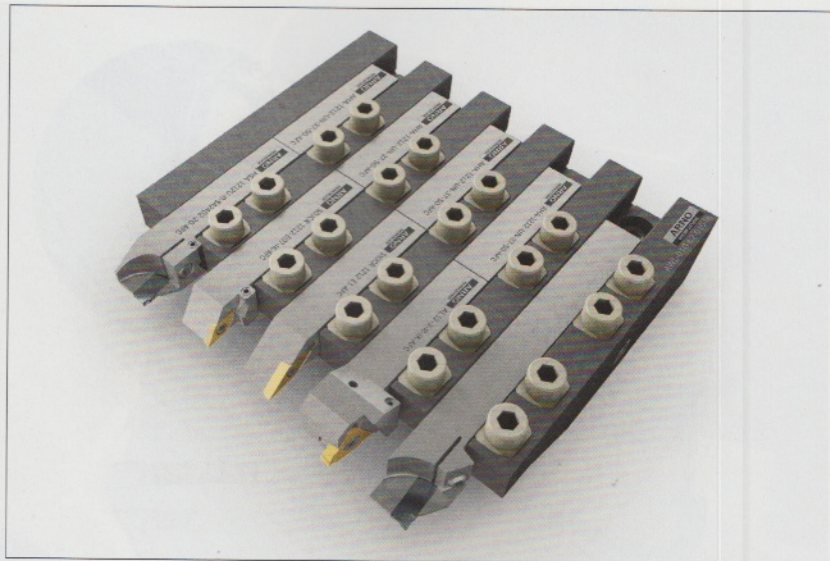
Das Werkzeugaufnahmesystem AWL hat eine integrierte Kühlmittelzufuhr.
